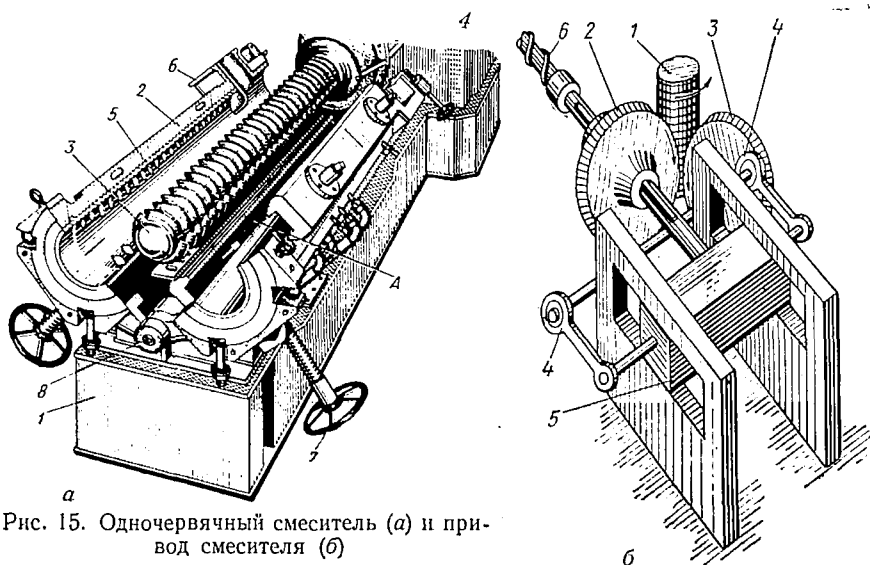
Одночервячный смеситель (а) и привод смесителя (б)
